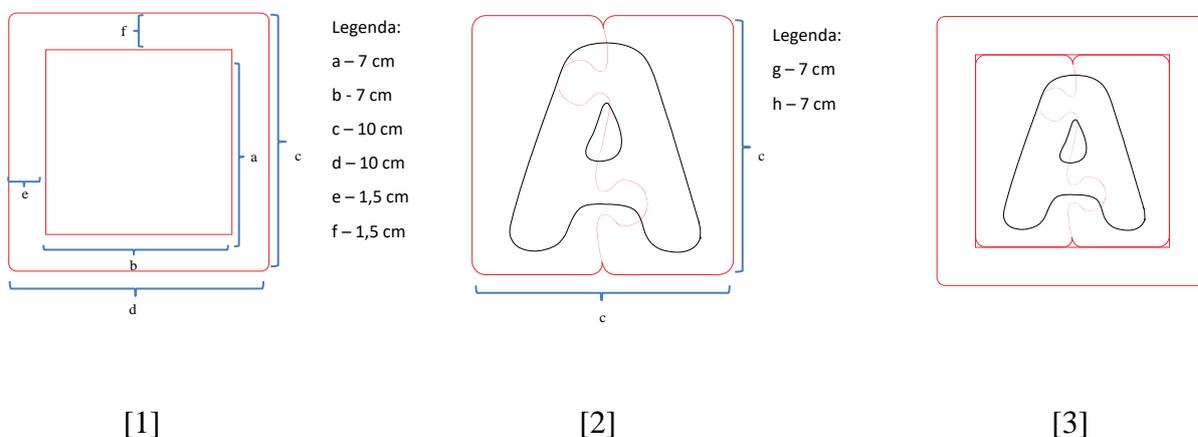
[1] Medidas da Moldura, [2] Medidas do Puzzle, [3] Peça final = Moldura + Puzzle
